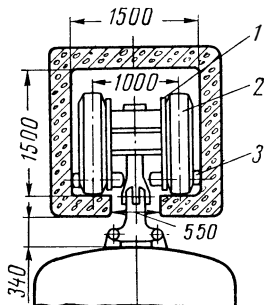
Компонировочная схема тележки с колесами на пневматических шинах:
